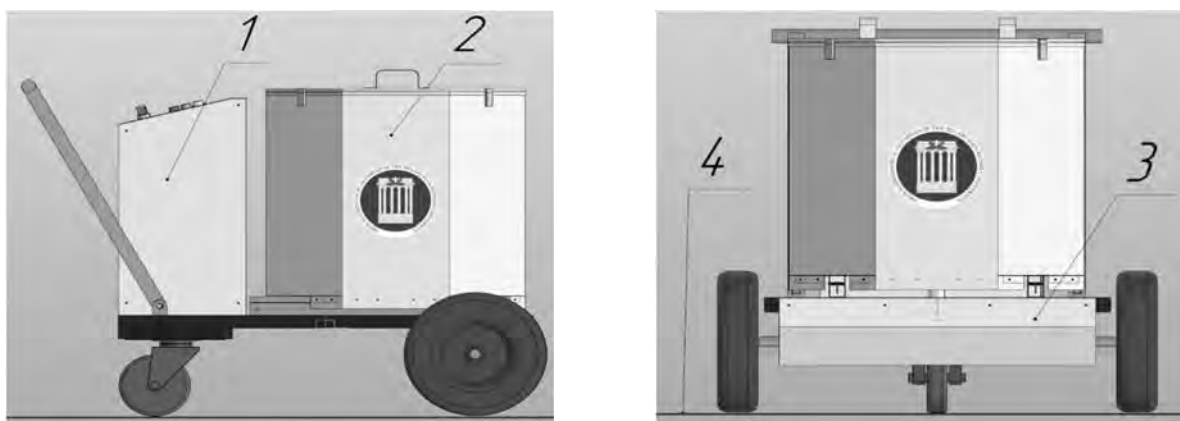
3D-модель молочного такси КОМПАС-3D/SOLIDWORKS: 1 – блок управления молочным такси; 2 – ёмкость молочного такси для транспортировки жидкой кормовой смеси; 3 – моторный отсек молочного такси; 4 – поверхность
